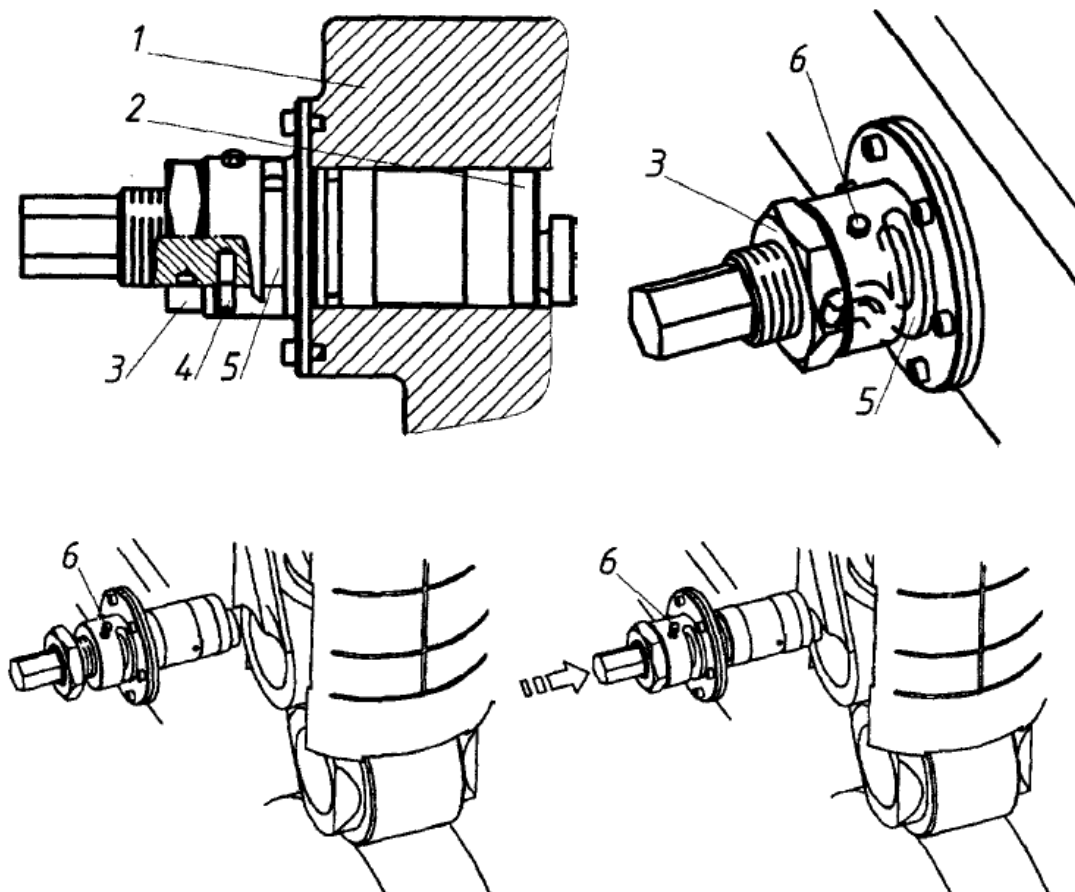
Підйомний і фіксуючий пристрій штовхача ПНВТ
